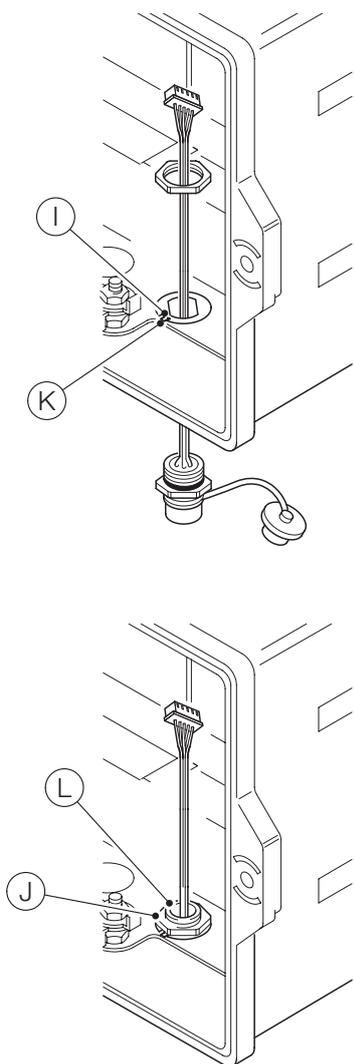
Крепление соединительного кабеля EZLink в сборе
